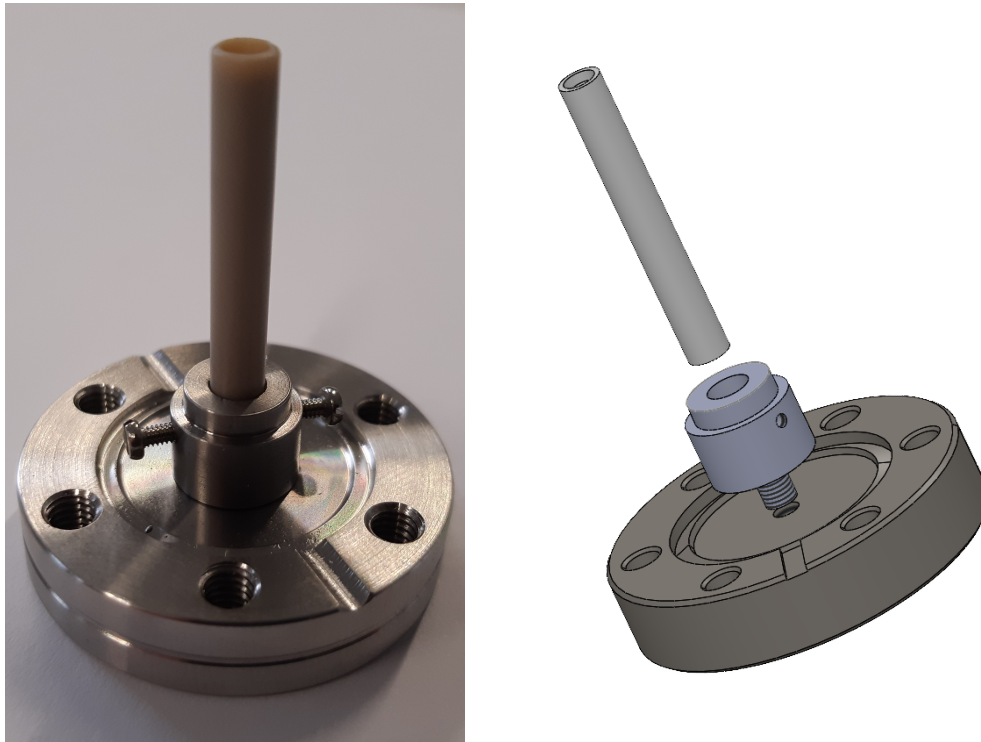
Darstellung des modularen Probenhalters für salzartige Proben (Höhe(gesamt) = 37,5 mm). Fotografie (links) und technische Explosionszeichnung (rechts, erstellt mit SolidWorks).
